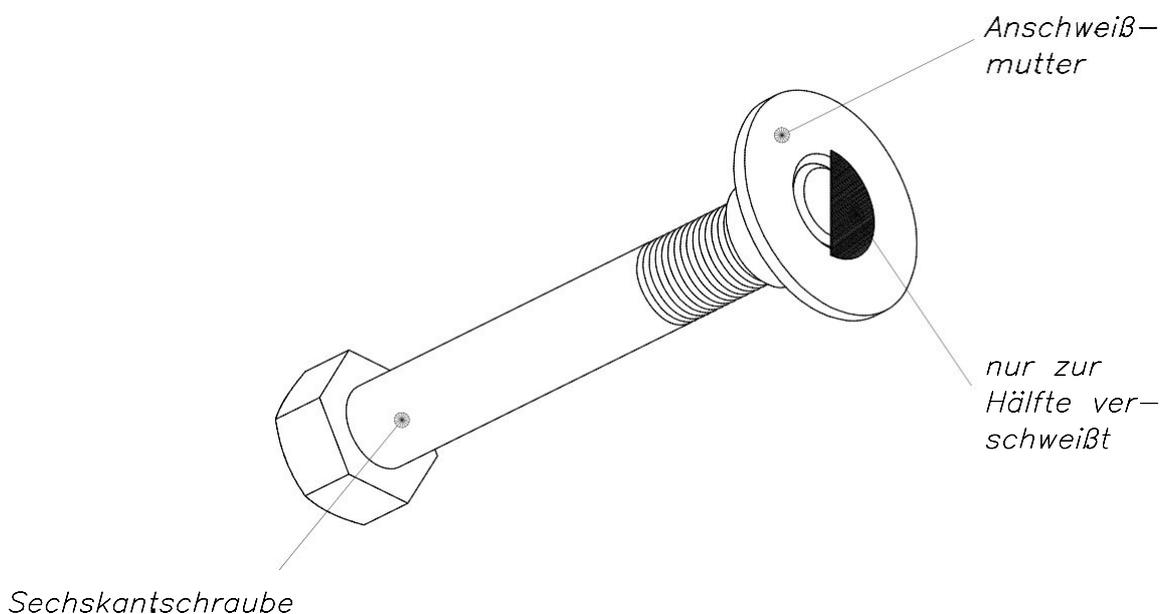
Beispiel einer inneren Verschweißung
